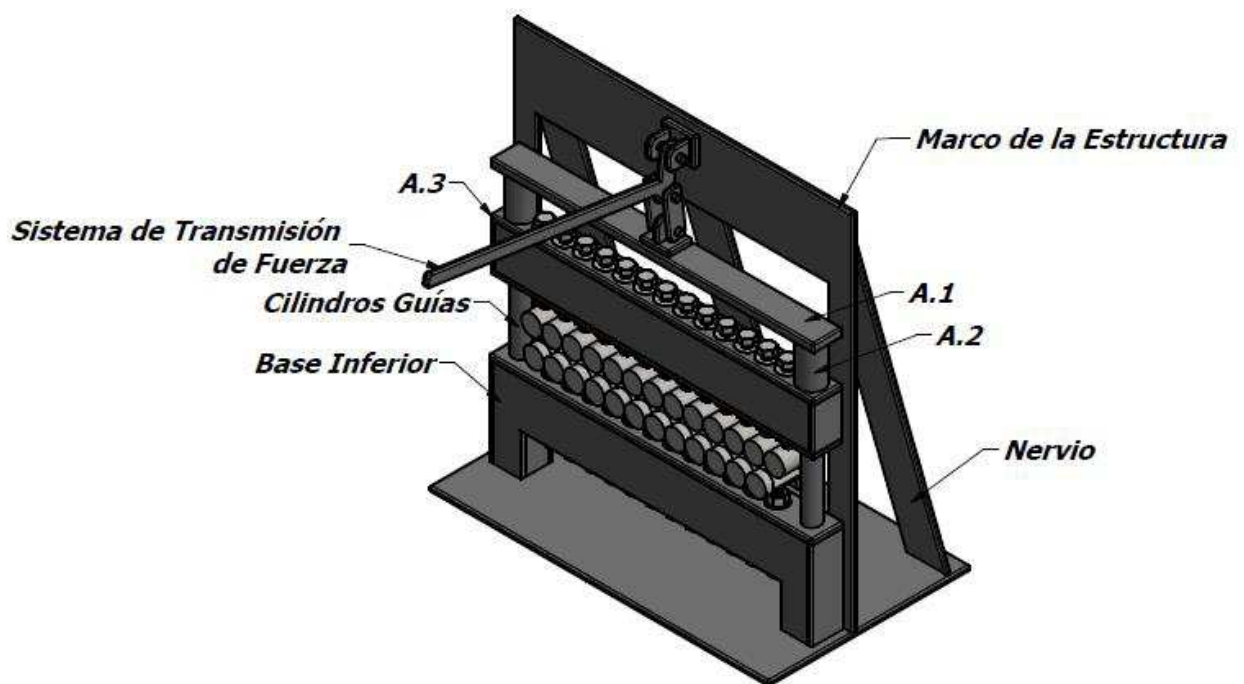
Vista isométrica de la máquina dobladora de placas de fijación.
